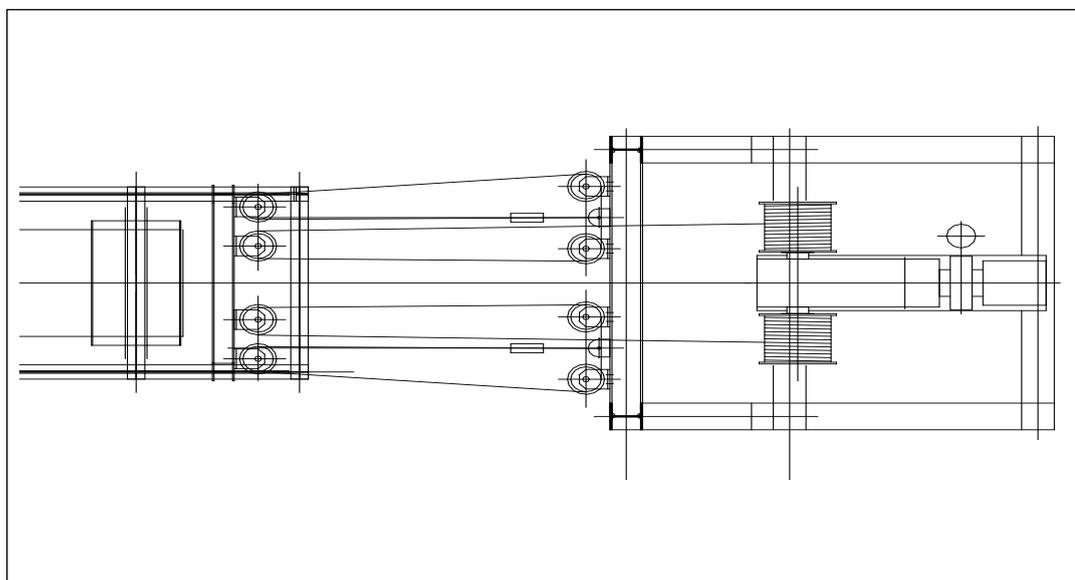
Эскизный чертеж лебедка натяжения ленты
